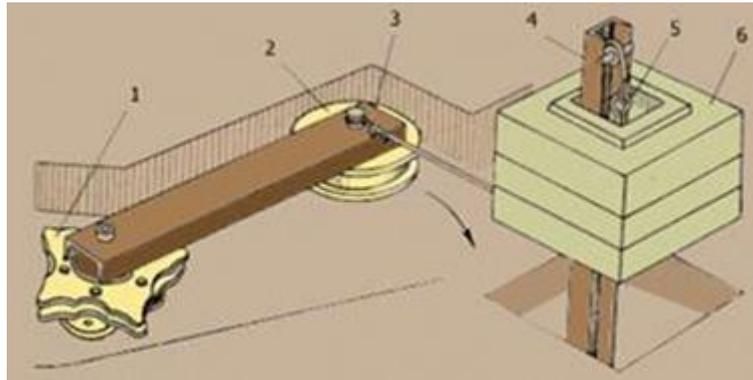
Автоматичний натяжний пристрій конвеєра КСГ-7:
